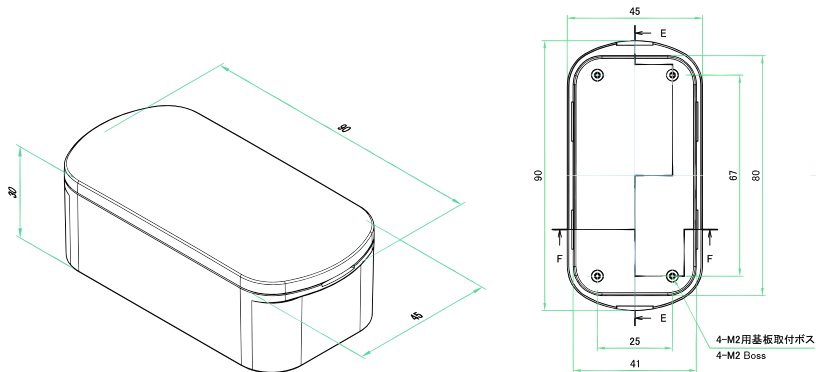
Dimensions du SIC5-9-3B TAKACHI.
